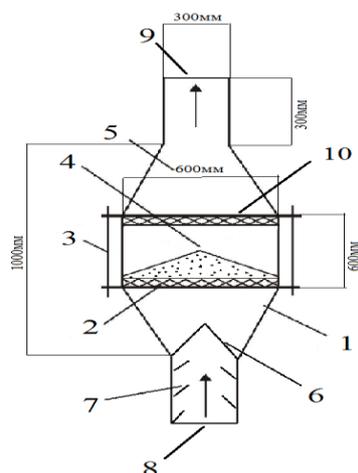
Устройство для обеззараживания и очистки воздуха
